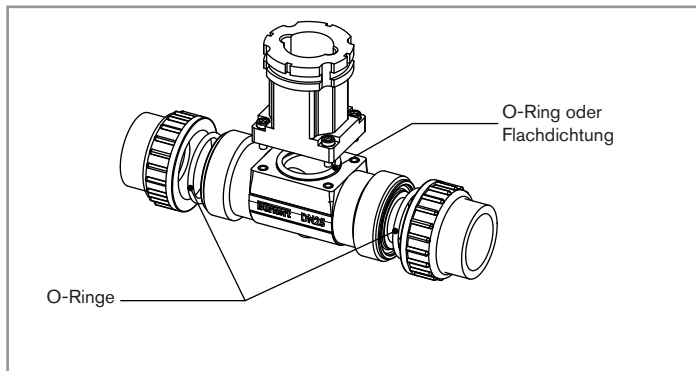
Dichtungen eines T-Fittings mit Klebe- oder Schweißverbindern
